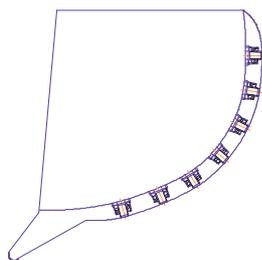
Ковш экскаватора с обратной лопатой, оборудованный пакетными пьезокерамическими трансдюсерами
